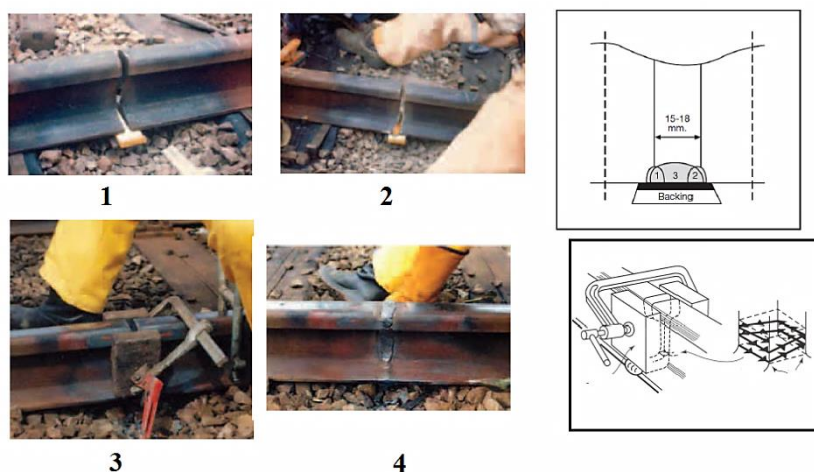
Технология ручной дуговой сварки рельса, разработанная фирмой ESAB
